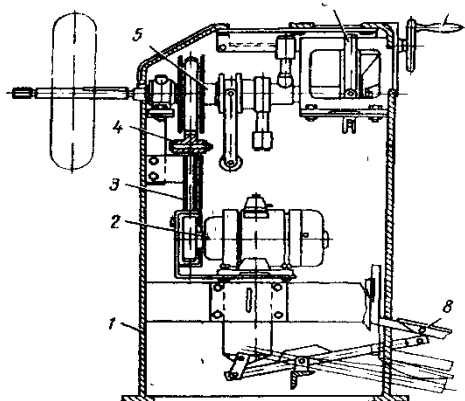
Станок для динамической балансировки колёс, модель 191:
